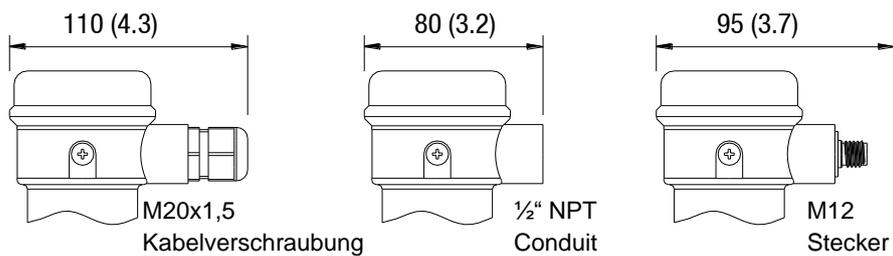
Mögliche Anschlussvarianten für Gehäuse Ø 65 mm
